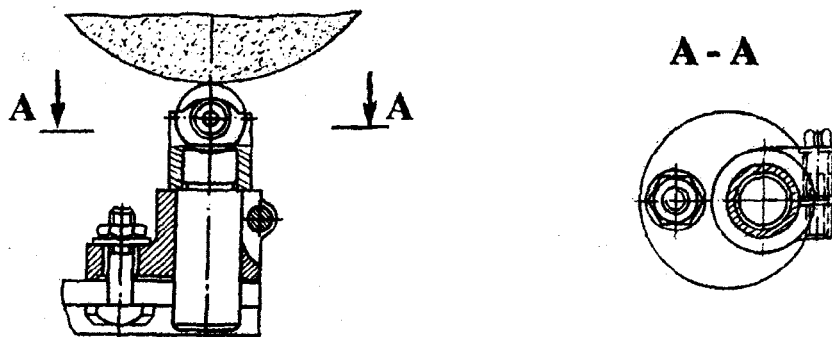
Установка приспособления с правящим инструментом на станке
